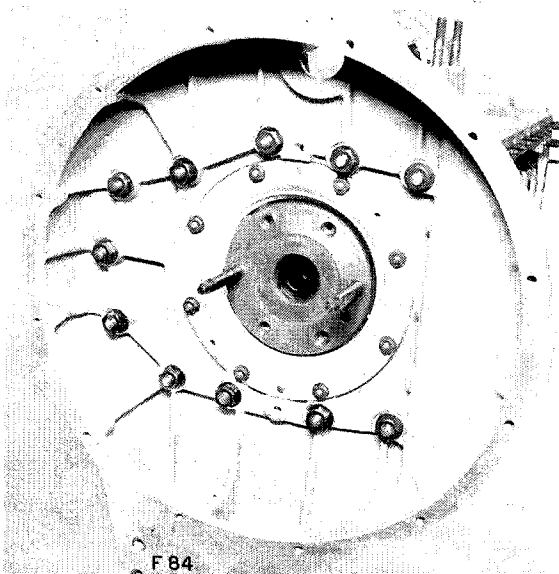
Schwungradgehäuse mit Kurbelwellenflansch und eingedrehten Montagebolzen
